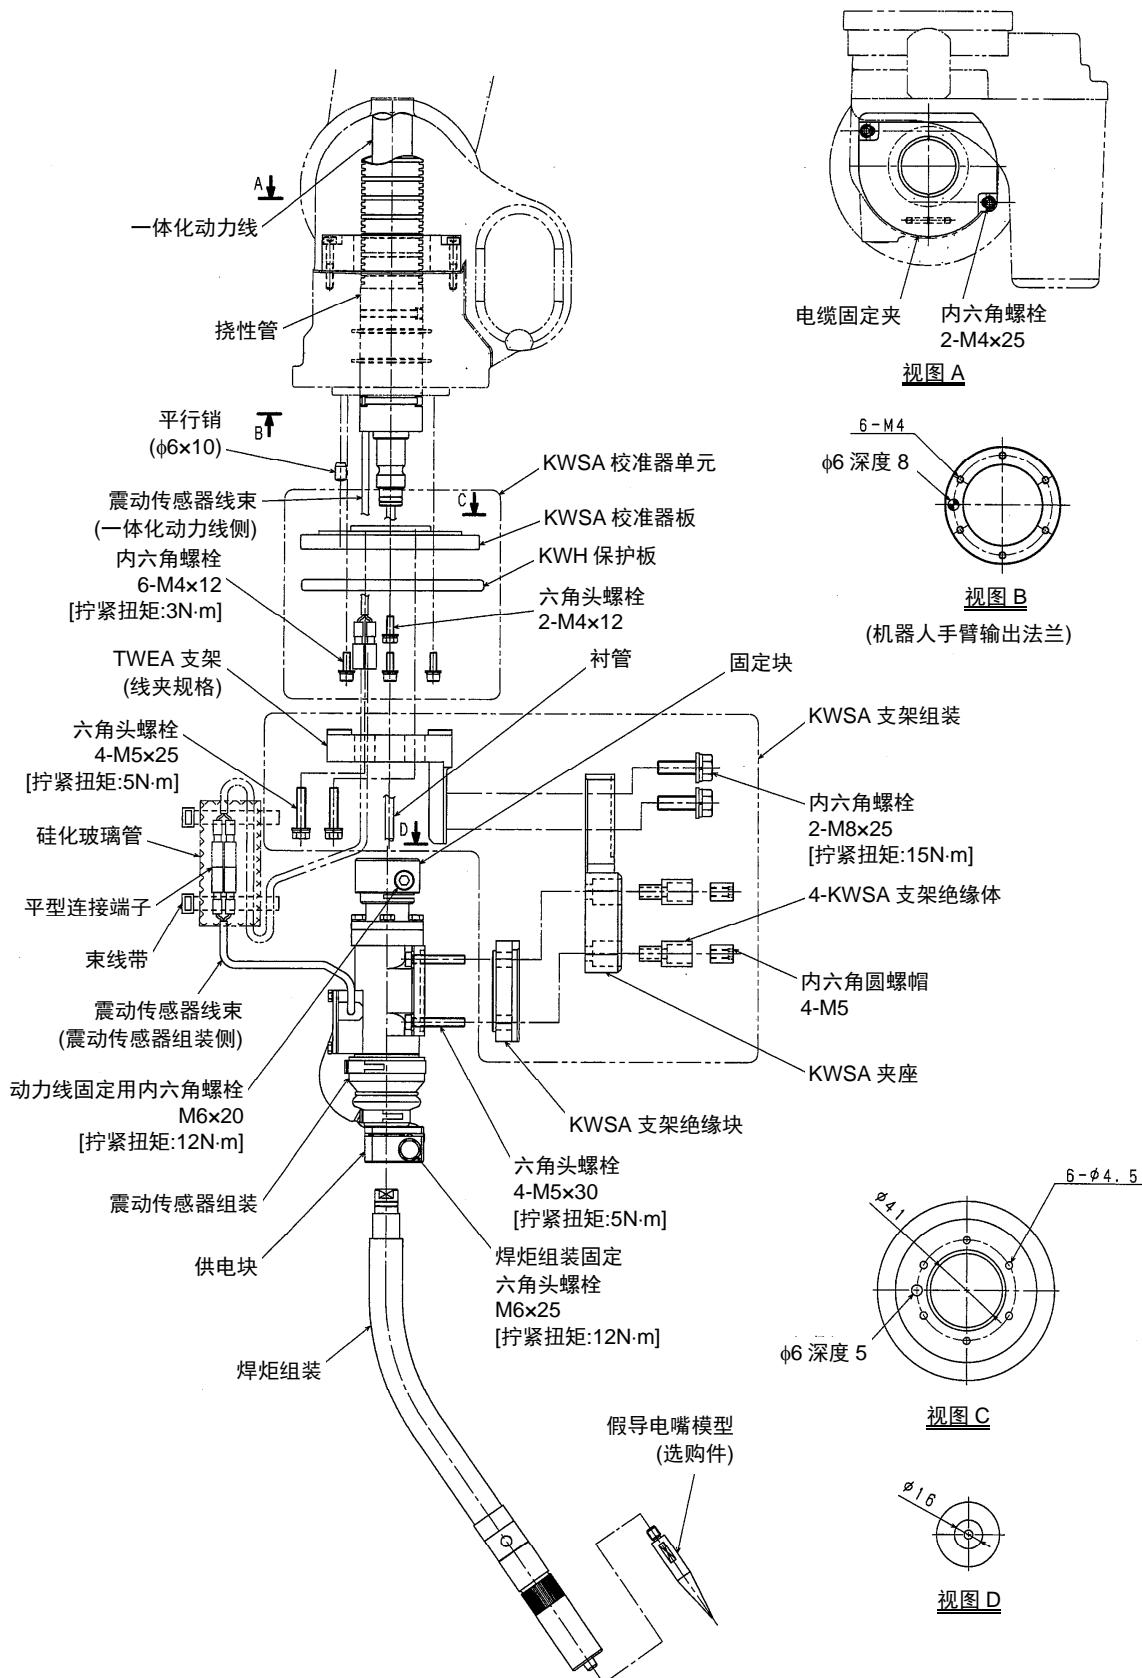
TOKIN 公司生产的焊炬及震动传感器的安装(G-type)
